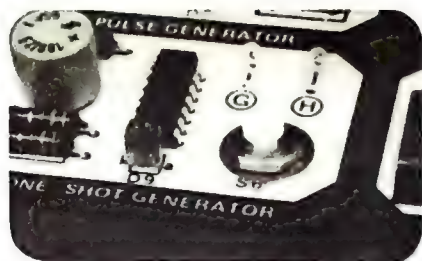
Bestückung im Feld One Shot Generator. Der Taster S6 wird mit dem Print verschraubt. Zwei blanke Drahtstücke stellen die Verbindung zwischen seinen Anschlüssen und den betreffenden Lötäugen auf der Kupferseite des Prints her.
